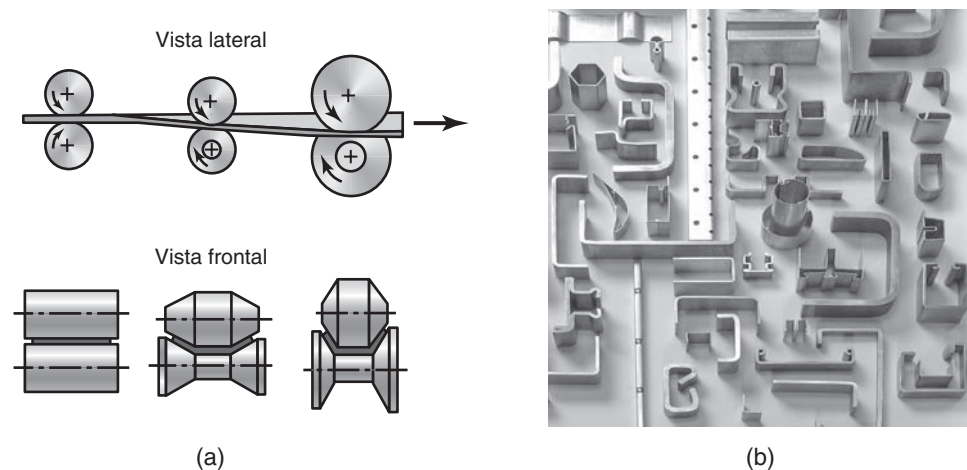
(a) Esquema del proceso de formado con rodillos. (b) Ejemplos de secciones transversales formadas con rodillos. Fuente: (b) Cortesía de Sharon Custom Metal Forming Inc.
